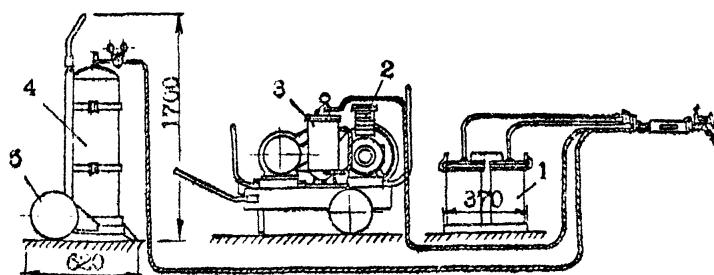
Схема расстановки комплекта оборудования для газопламенного напыления цинко-полимерных покрытий.
